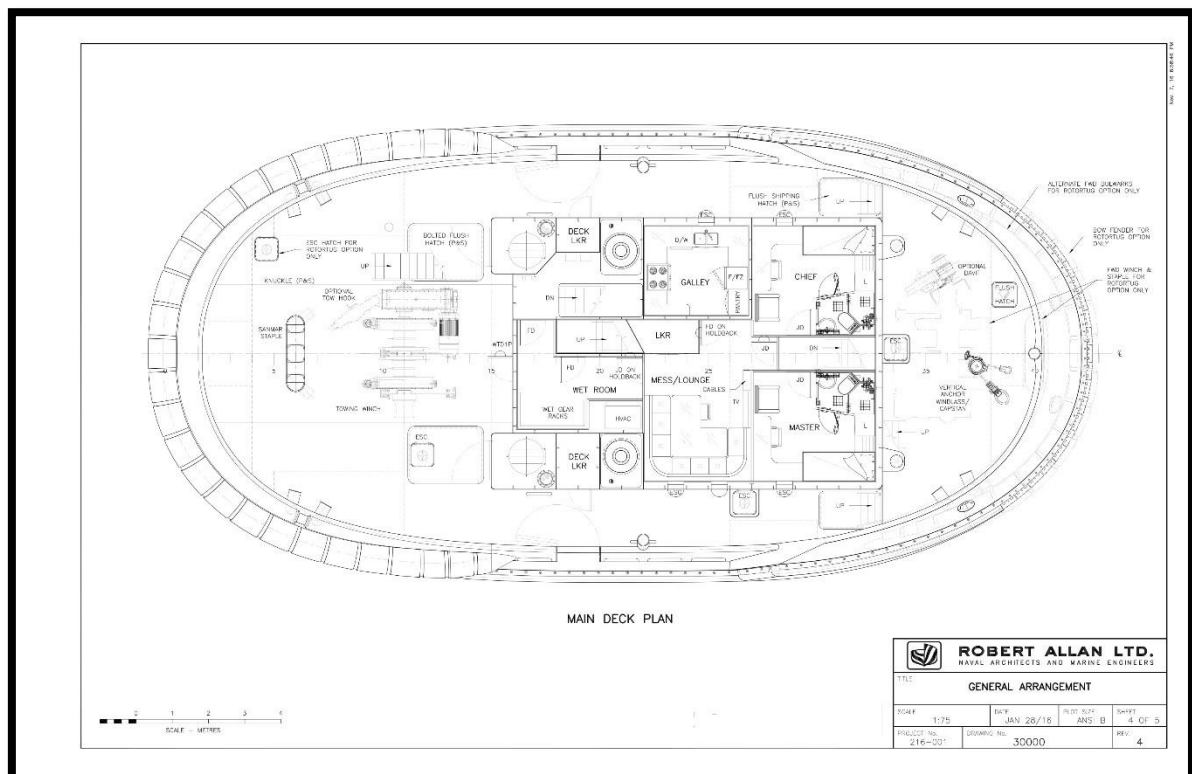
Main deck plan ROTORTUG ART 60-25 SX
